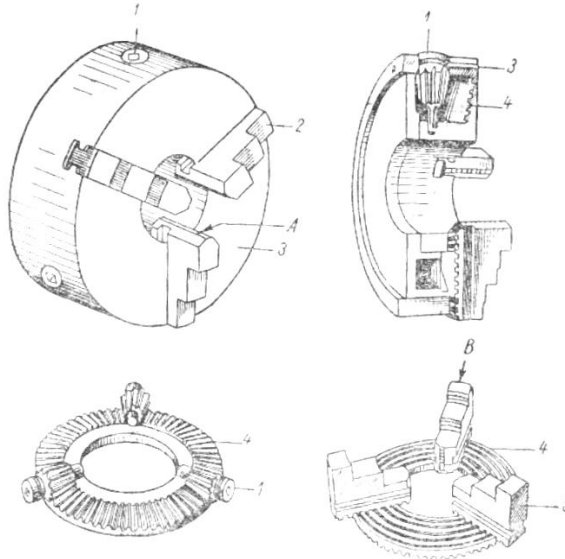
Спиральный самоцентрирующий трёхкулачковый патрон и его детали: 1-одна из трёх конических шестерён; 2-кулачки(прямые); 3-корпус патрона; 4-спиральная шестерня (спираль Архимеда); 5-кулачки (обратные)
